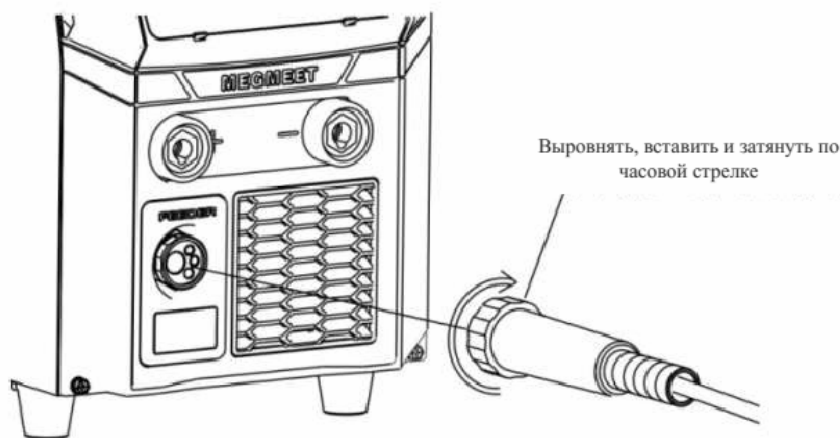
Схема подключения сварочной горелки
